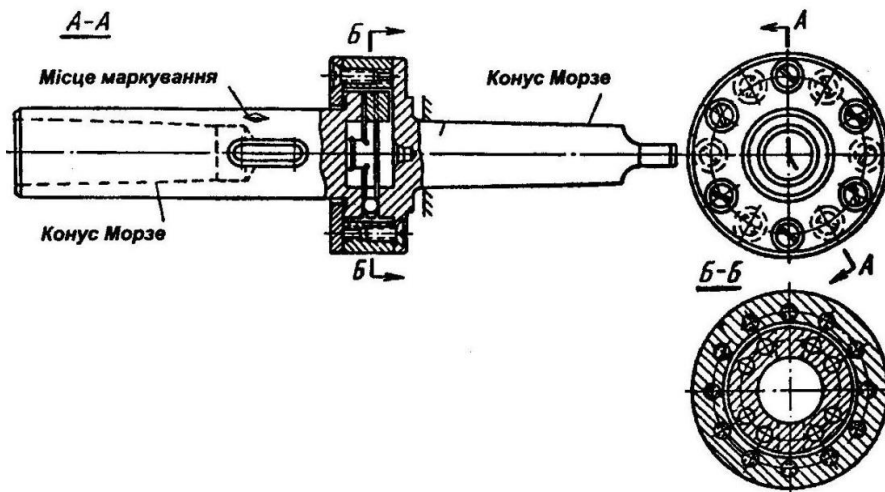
Плаваючий патрон для інструмента з конічним хвостовиком, швидкозмінний
